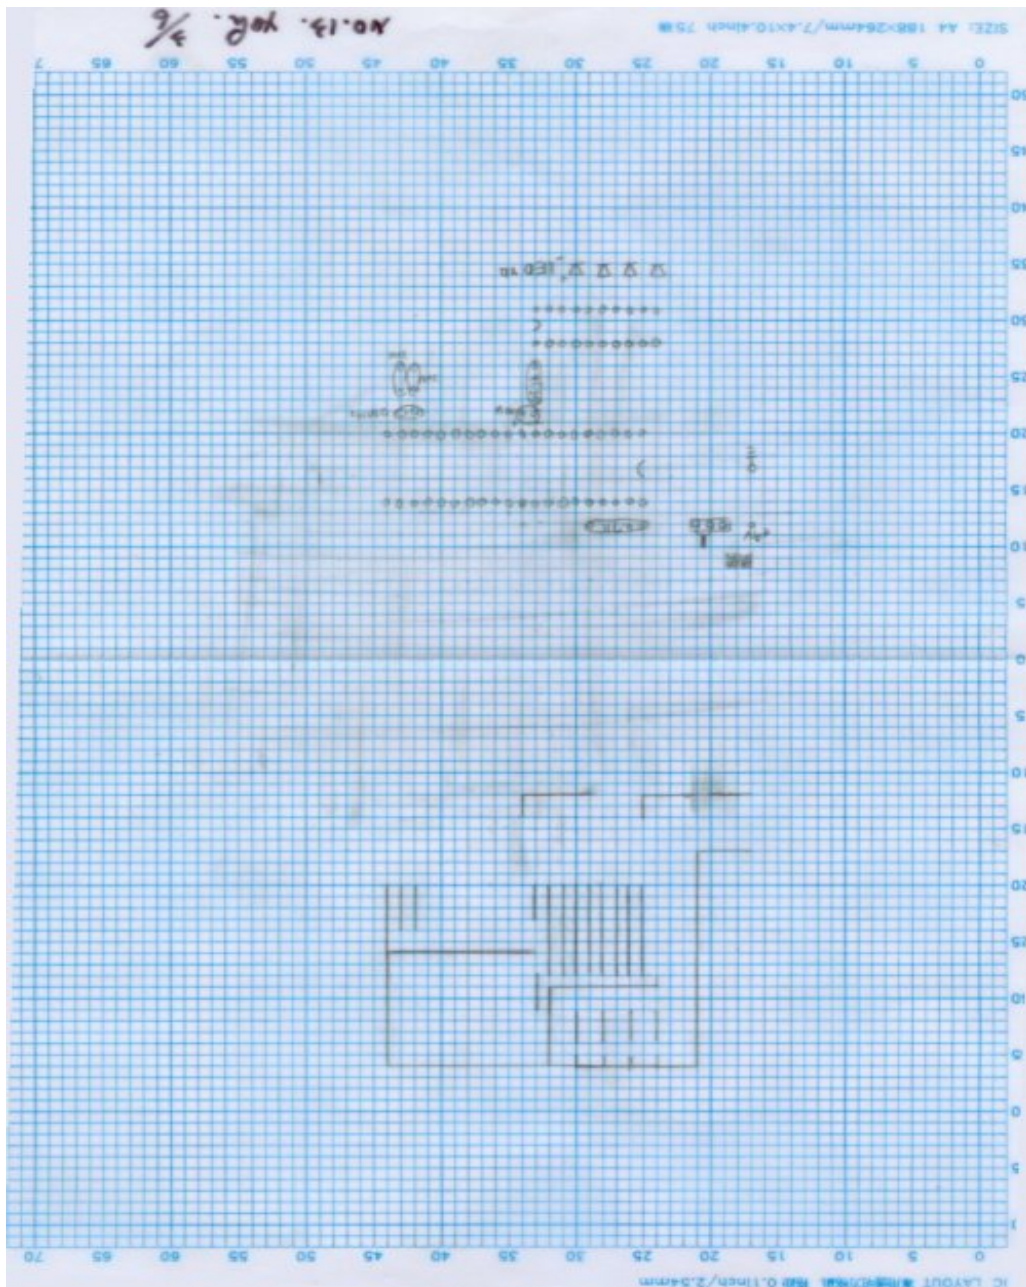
電子密碼鎖之電路板 Layout 圖
